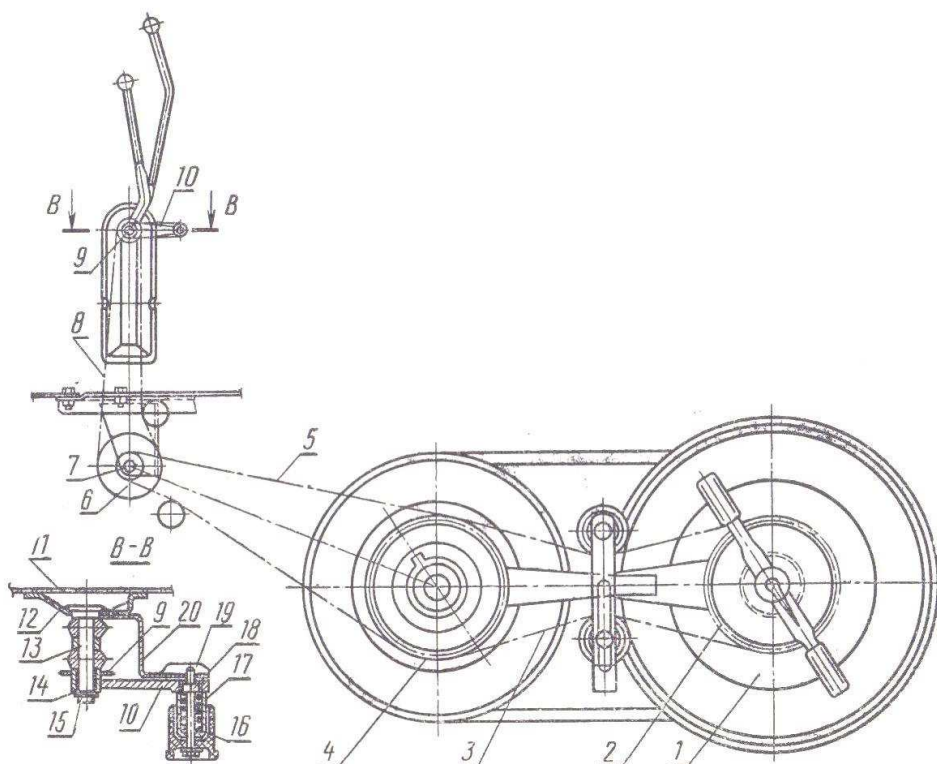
Механизм дистанционного управления частотой вращения барабана комбайна СК-5: 1 – главный контрпривод; 2, 4, 6, 7, 9 – звездочки; 3, 5, 8 – приводные цепи; 10 – рычаг; 11 – бункер; 12 – накладка; 13 – ось; 14 – шайба; 15 – замочное кольцо; 16 – пружина; 17 – втулка; 18 – фиксатор; 19 – кронштейн; 20 – накладка
